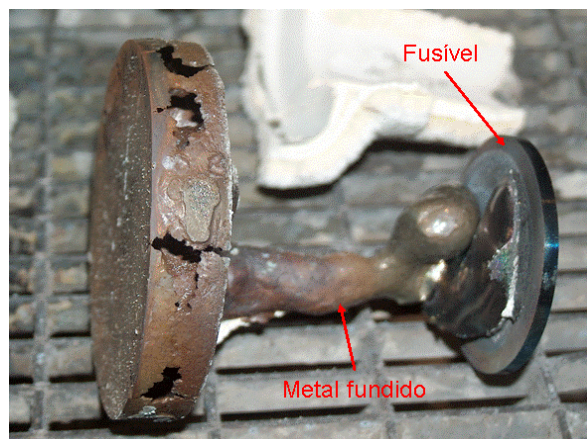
Fusível que não fundiu em contacto com metal fundido.
